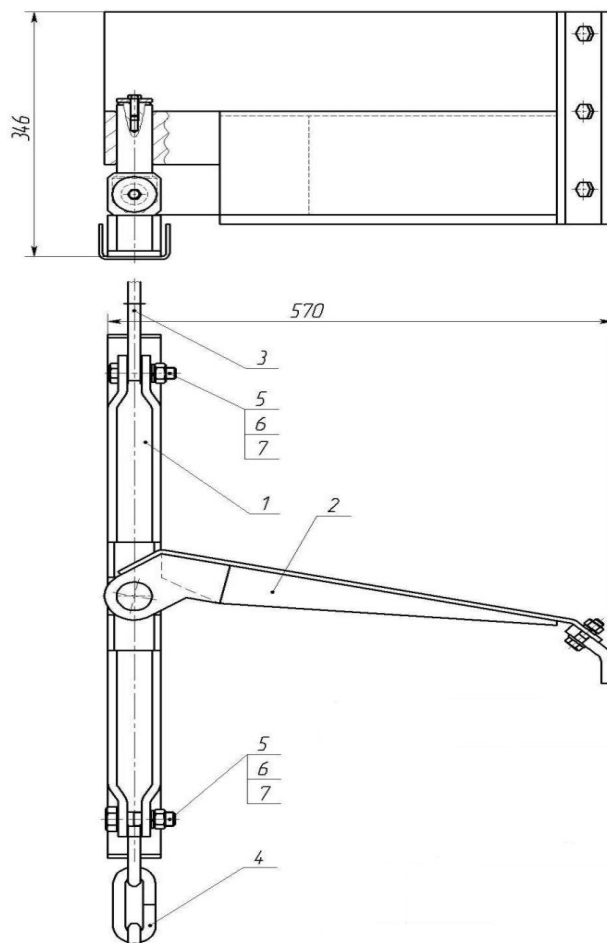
Схема консольного скрепера навозоуборочного транспортера: 1 – ползун; 2 – скребок; 3 – штанга; 4 – цепь; 5, 6, 7 – болтовые соединения
